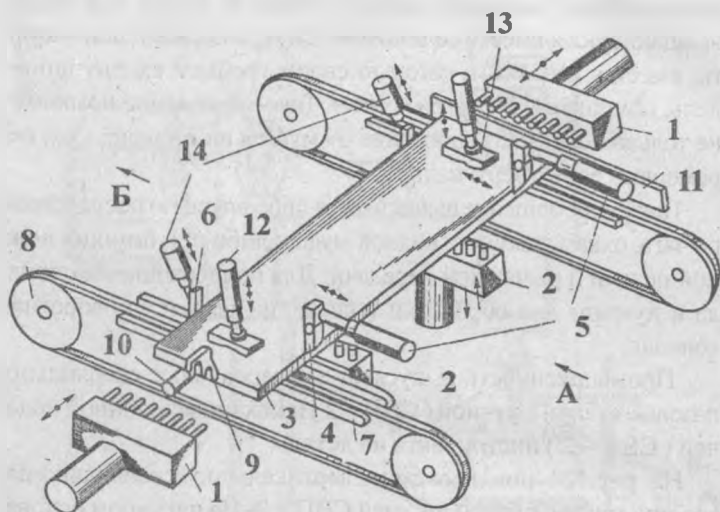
Схема многошпиндельного сверлильно-присадочного станка: 1-горизонтальные сверлильные головки; 2-вертикальные сверлильные головки; 3-заготовка; 4-толкатели; 5 пневмоцилиндры; 6-упоры; 7-линейка главной опорной базы; 8-конвейер; 9-торцовые упоры; 10-пневмоцилиндр; 11-упоры; 12-пневмоцилиндры вертикального прижима; 13-башмак; 14-пневмоцилиндры торцевых прижимов
